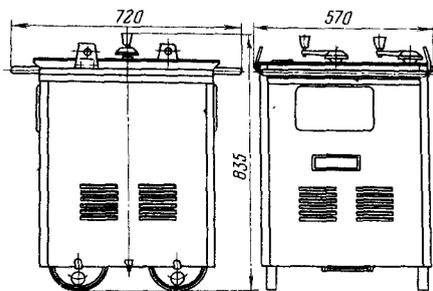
Однопостовой сварочный трансформатор для дуговой сварки ТД-300
